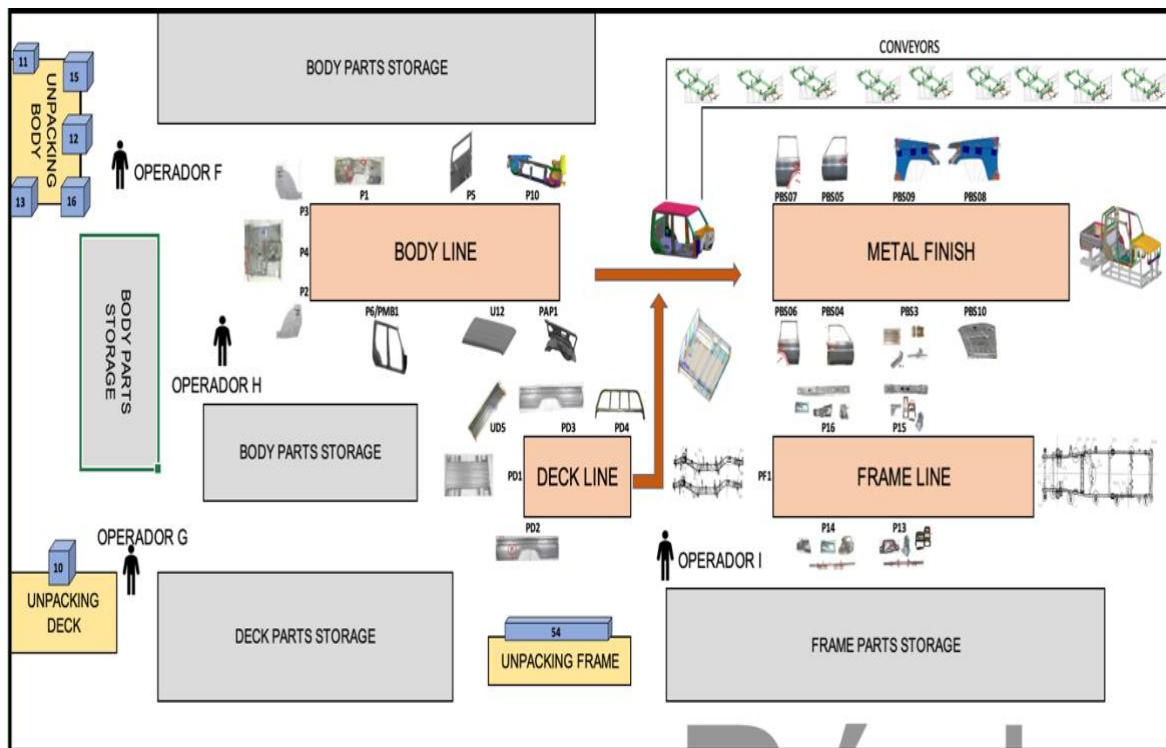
Layout simplificado da seção de soldadura com os colaboradores envolvidos
